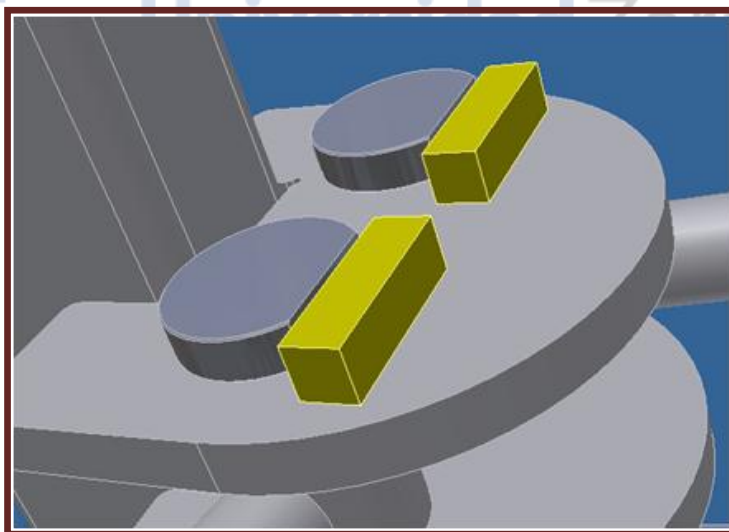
Figura. Chapa freno soldada en orejeta.
